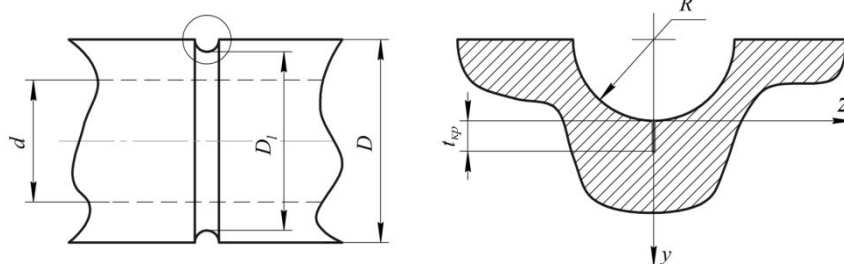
Цилиндрический образец с надрезом и нераспространяющаяся трещина усталости
